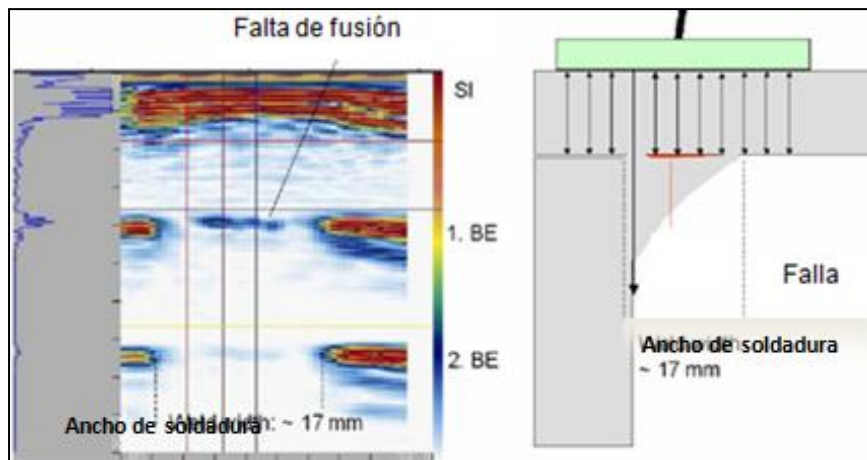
Escaneo de una soldadura en esquina vista en el escaneo B ^[13]
